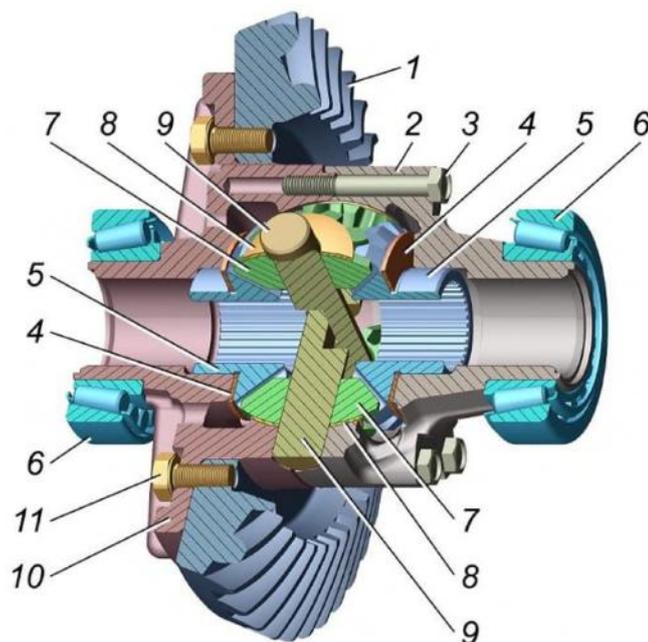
Дифференциал в сборе с ведомой шестерней: 1 – шестерня ведомая; 2- коробка сателлитов дифференциала правая; 3,11 - болты; 4 - шайба шестерни полуоси; 5 - шестерня полуоси; 6 – подшипник; 7 - сателлит; 8 - шайба сателлитов; 9 – ось сателлитов; 10 - коробки сателлитов дифференциала левая
